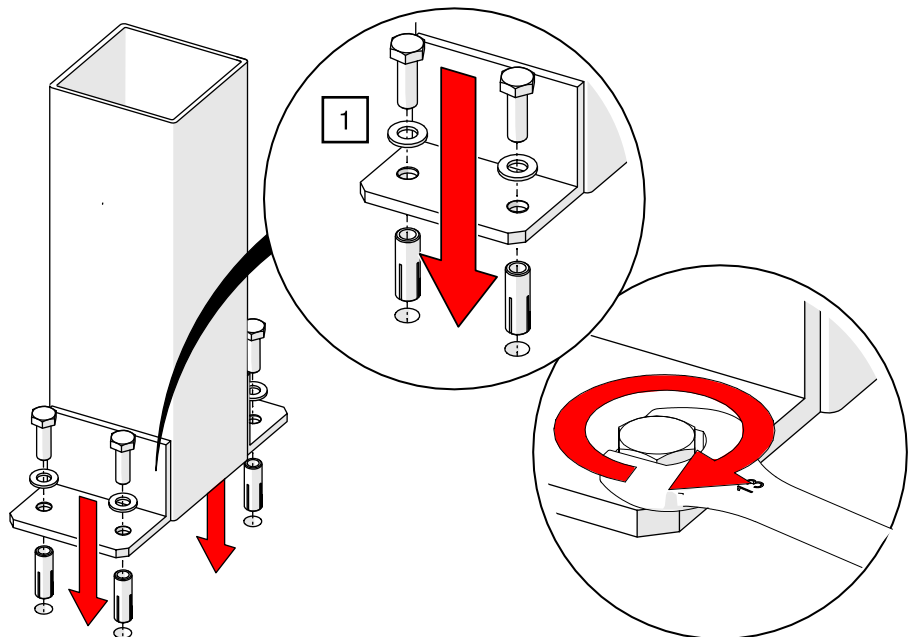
Gegenspannrolle mit Kontergewicht – Führungskorb verschrauben
